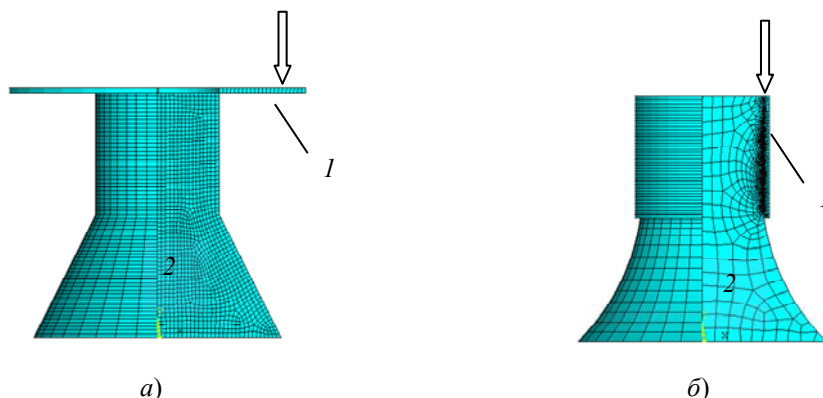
Схема формирования уплотнения: 1 – дисковая заготовка (а), заготовка в виде цилиндрической оболочки (б); 2 – оправка
